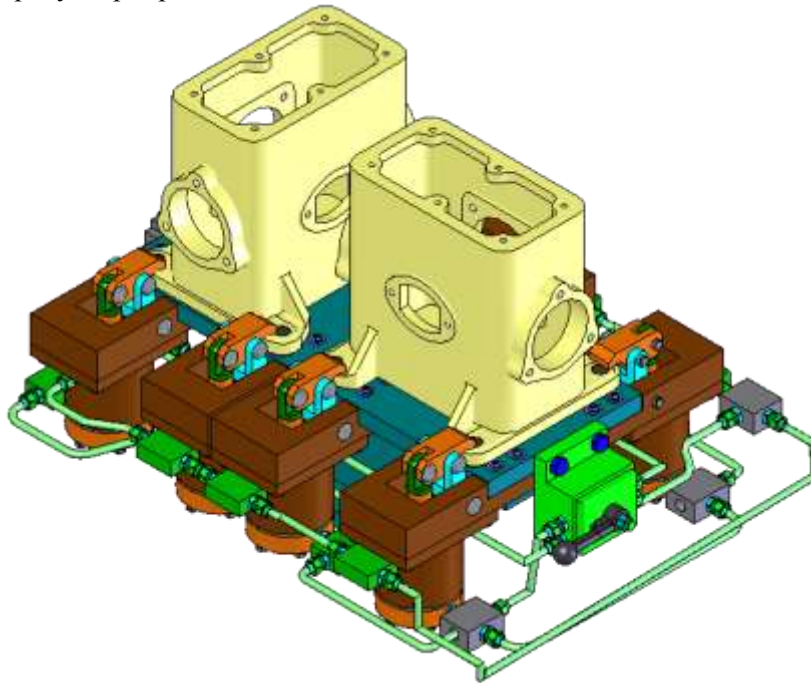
Ізометрія готового пристосування із закріпленими корпусами редуктора на ньому
